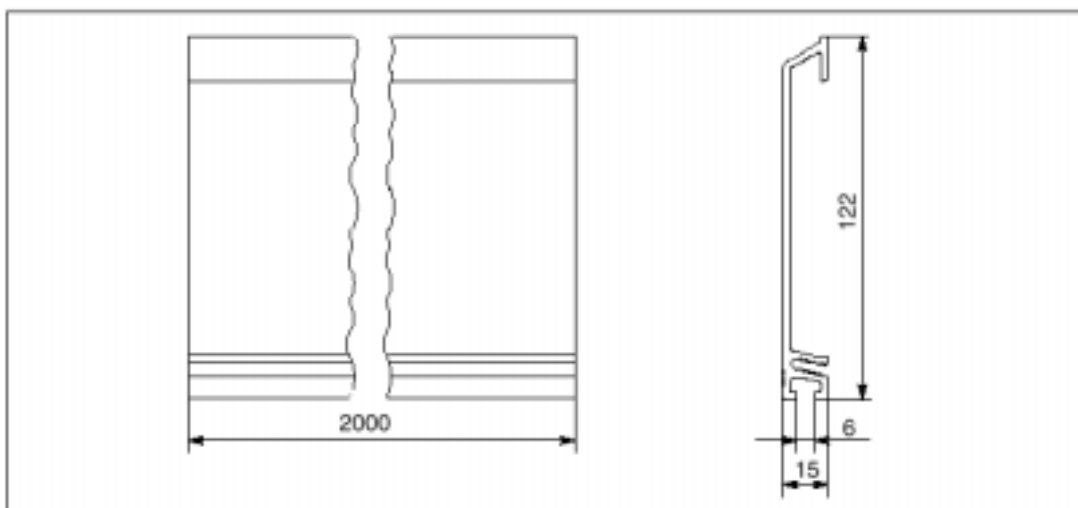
Чертеж с размерами 2000-миллиметровой профильной шины
